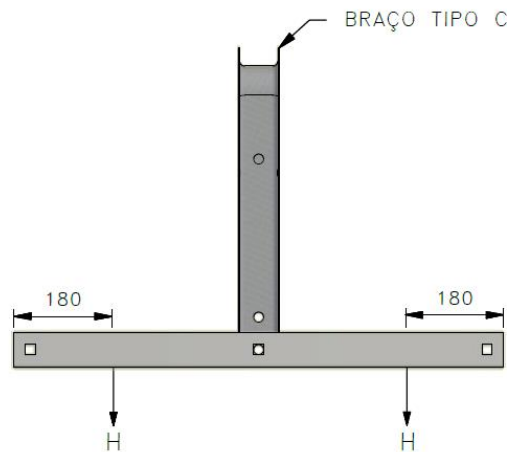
DETALHE PARA EXECUÇÃO DO ENSAIO
